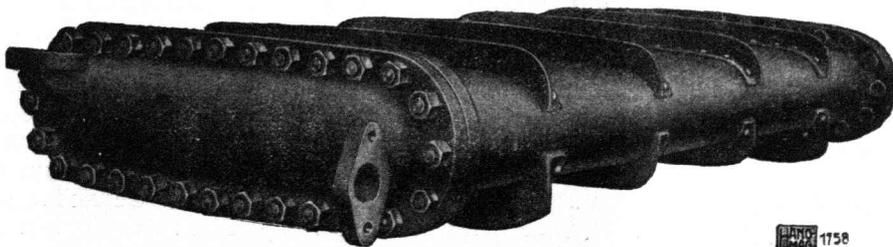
Ansicht des geschlossenen Speisewasser-Vorwärmers, Bauart Schichau.
